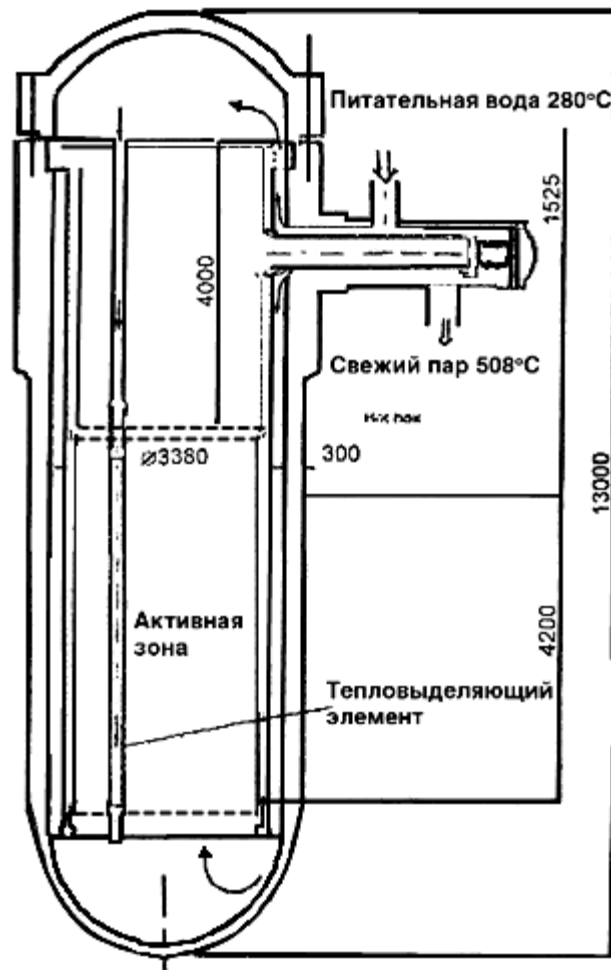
Корпус давления легководного реактора со сверхкритическими параметрами пара
